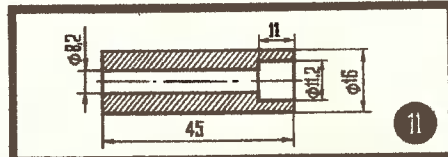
Втулка для крепления съёмника при выпрессовке коленчатого вала (2 шт.).
